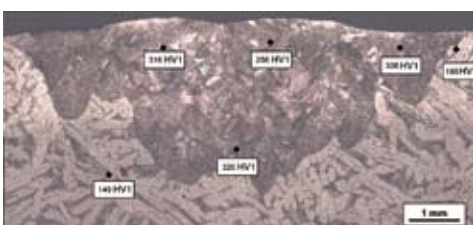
Querschliff einer manuellen Laserstrahlschweißung ohne Unregelmäßigkeiten
